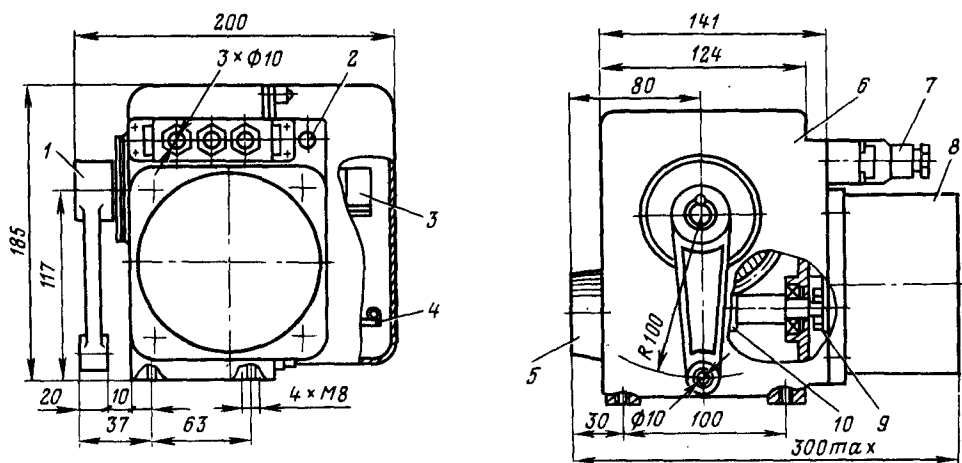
Общий вид, габаритные и присоединительные размеры исполнительного механизма МЭО с электродвигателем ДРС:
